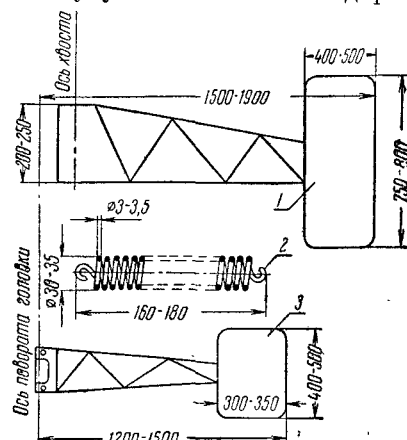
Размеры хвоста, бокового плана и пружины для ветроустановки с поршневым насосом:
